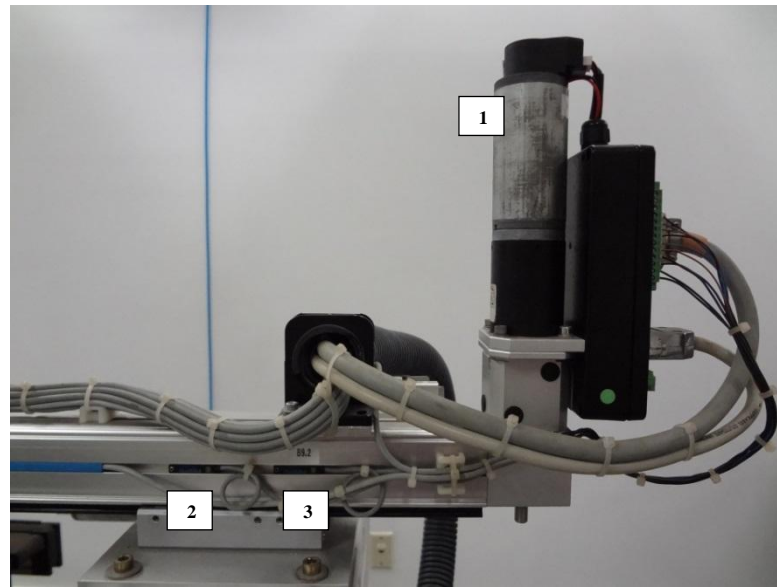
Detalhe do eixo X com: 1 - servo motor; 2 e 3 - Sensores de calibração do controlador;
